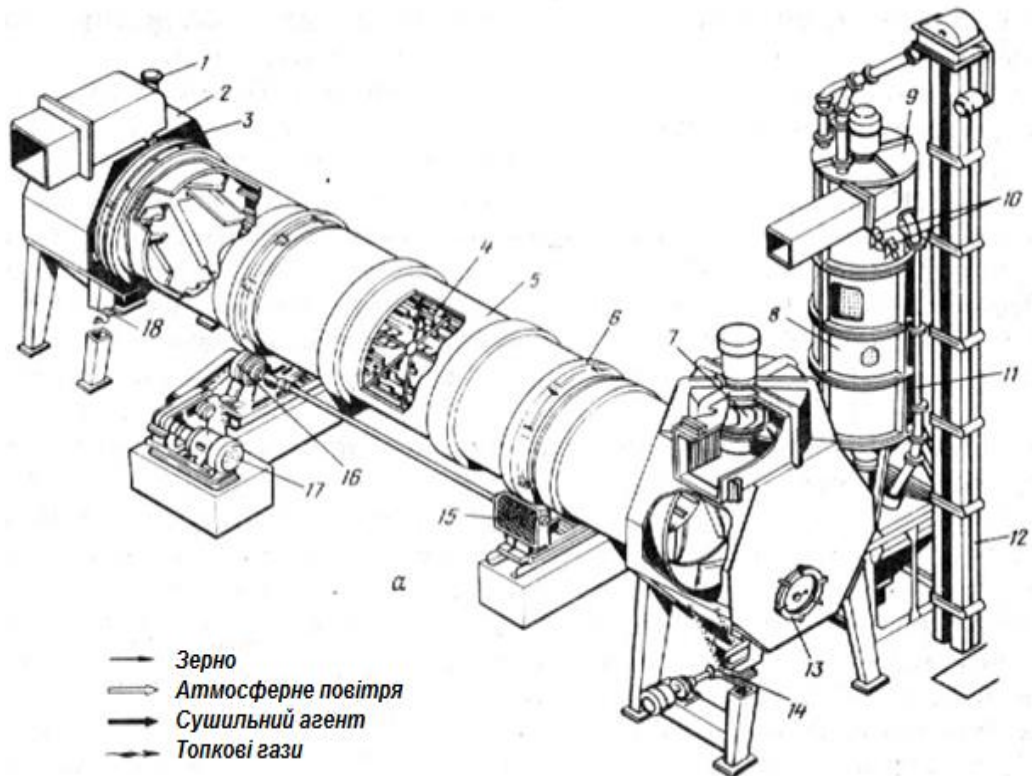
Барабанна сушарка для зерна СЗСБ-8А
